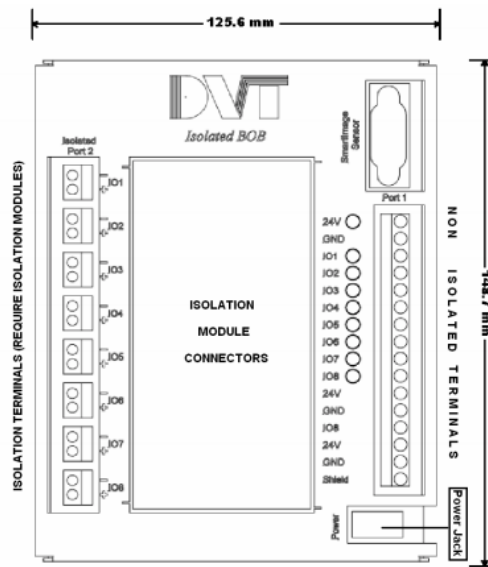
Dimensiones del módulo DVT Isolated Breakout Board. [16]
